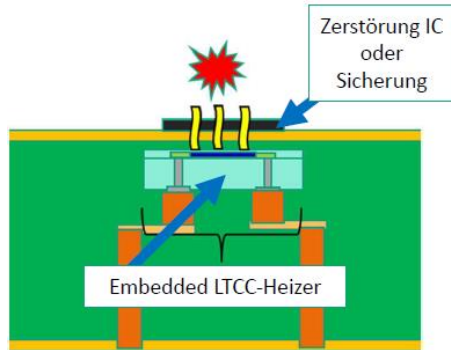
Illustration eines Heizelementes integriert in PCB, Seitenansicht
